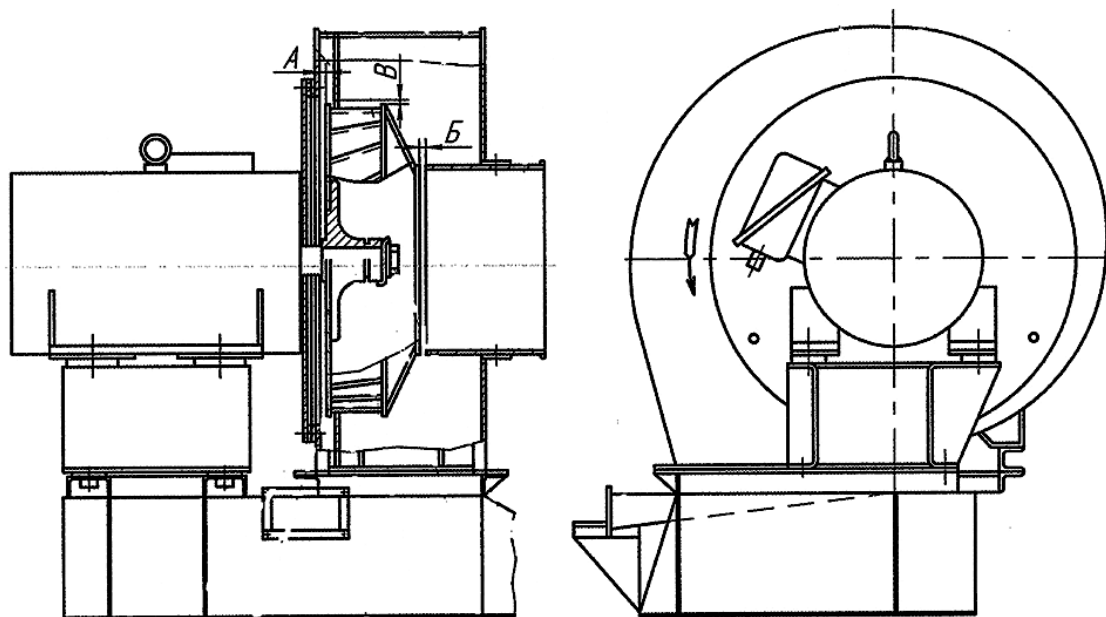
Блок центробежного вентилятора-воздухоочистителя ЦВ9-37,6-7,6
